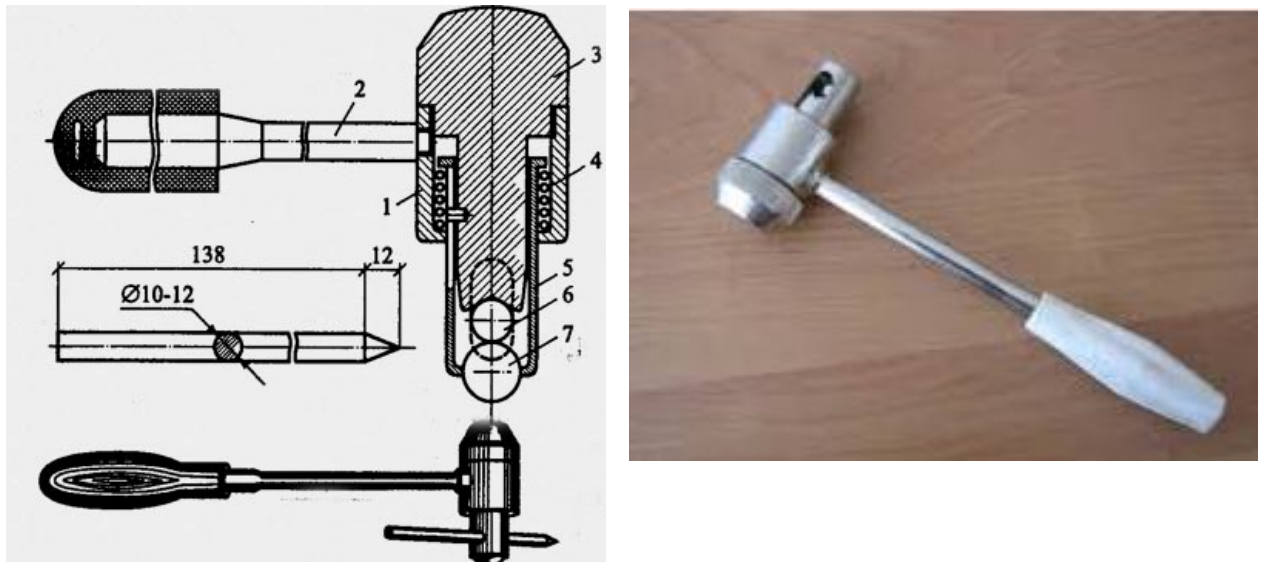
Схема еталонного молотка К. П. Кашкарова: 1 - корпус; 2 - руків'я; 3 - голівка; 4 - пружина; 5 - склянка з отворами для кульки 7 і еталонного стержня 6.
